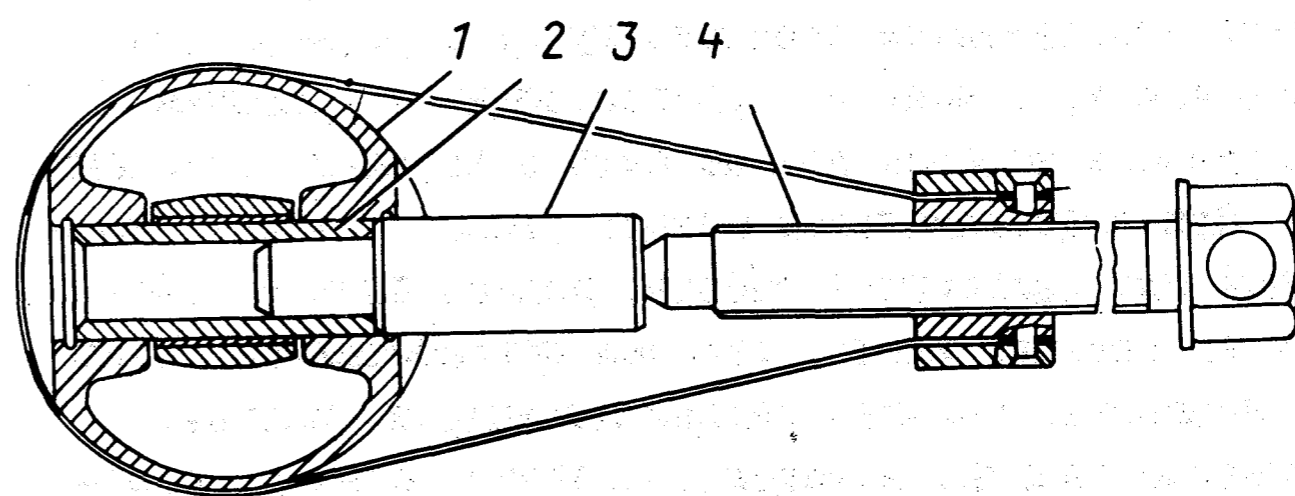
Выпрессовка поршневого пальца из поршня съемником 7823-6102:
